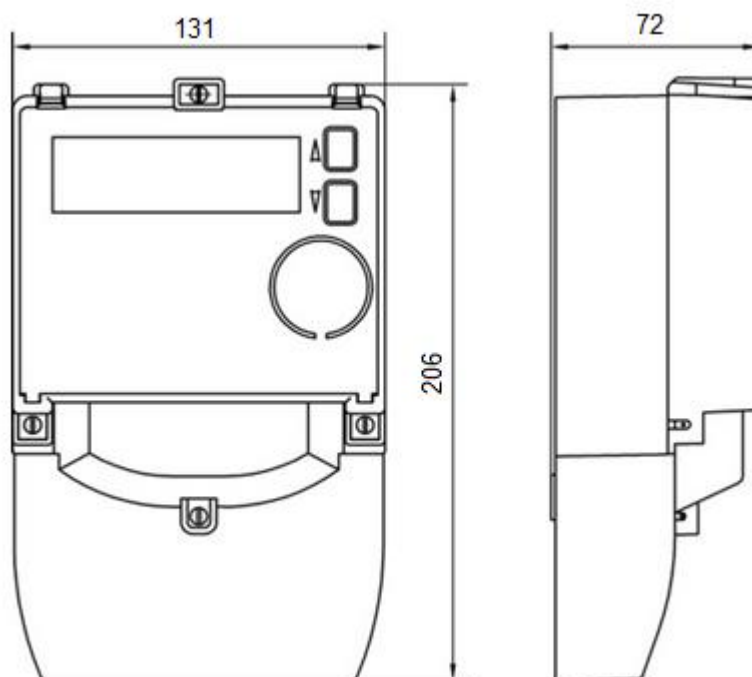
Габаритный чертеж счетчика «Меркурий 204»
